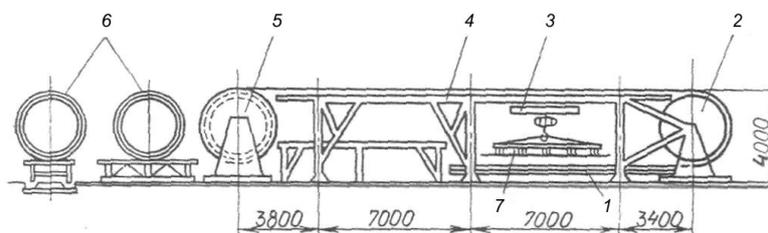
Универсальный станок для изготовления и сваривания полотнищ в рулоны:
